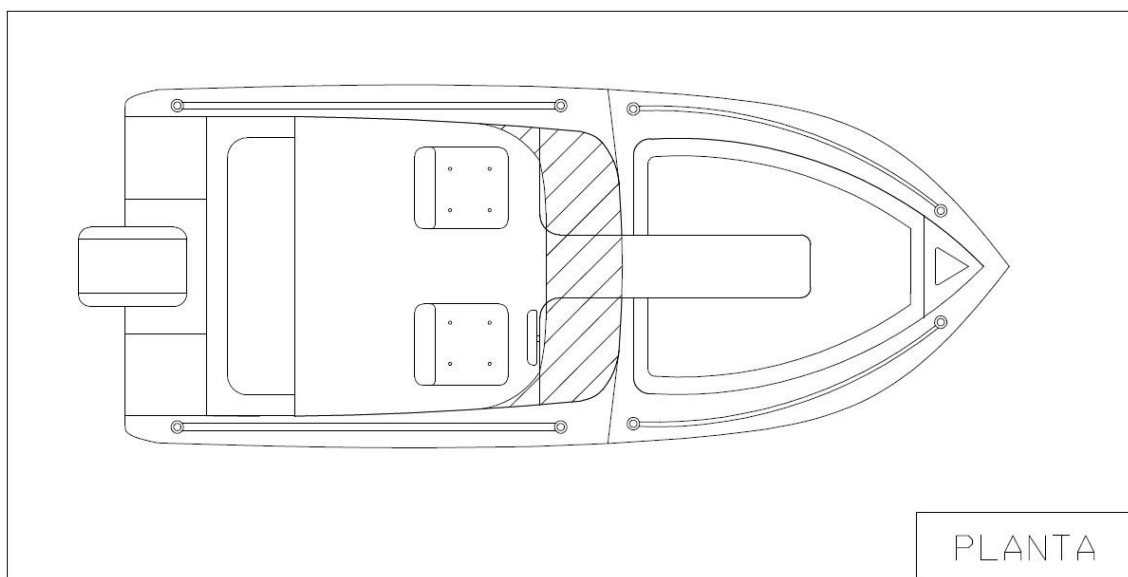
Vista en planta de la embarcación. FUEENTE PROPIA. Programa informático Autocad.
